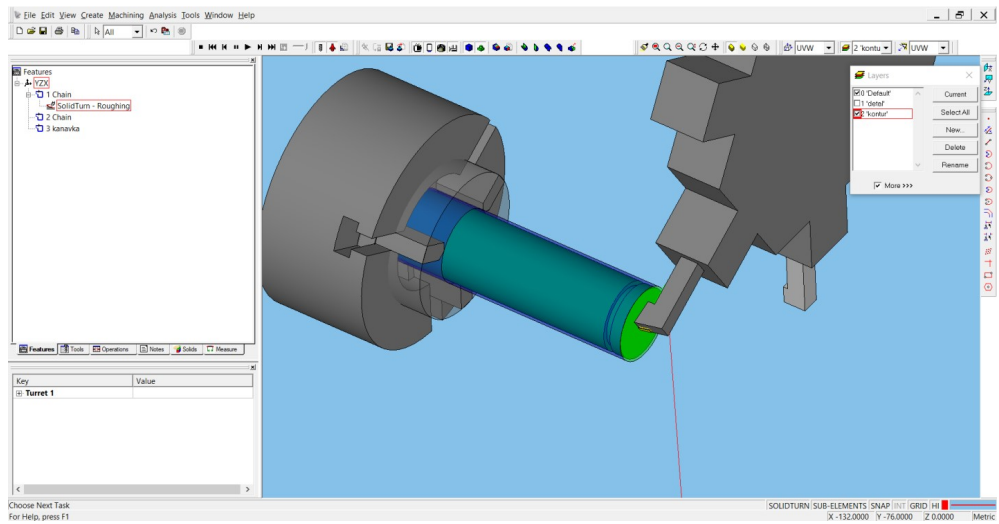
Траєкторія руху металорізального інструменту при обробленні контуру вала-шестерні
